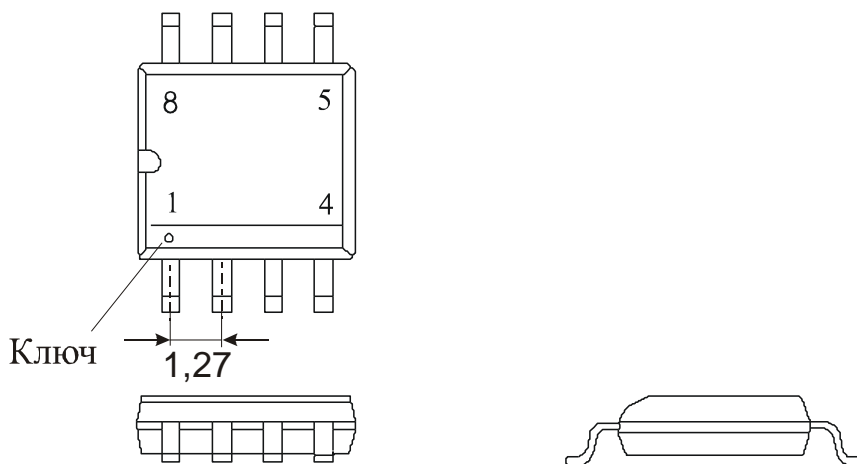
Конструкція пластмасового корпусу 4303 для поверхневого монтажу
